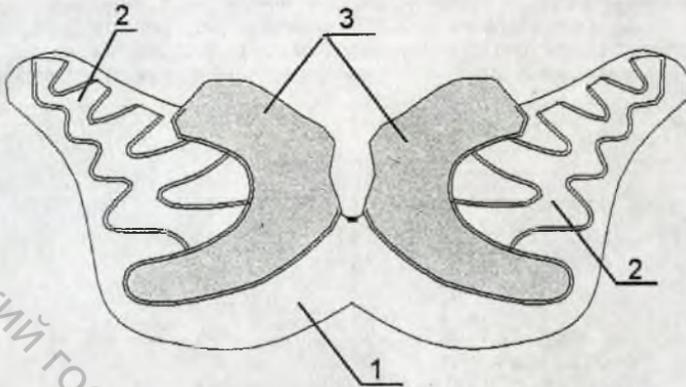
Элемент конструкции плоской заготовки верха мужской обуви
